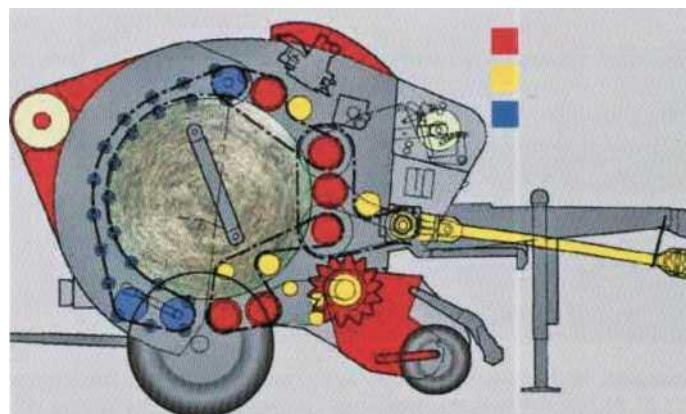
Схема компоновки рабочих органов пресс-подборщика Rollprofi
